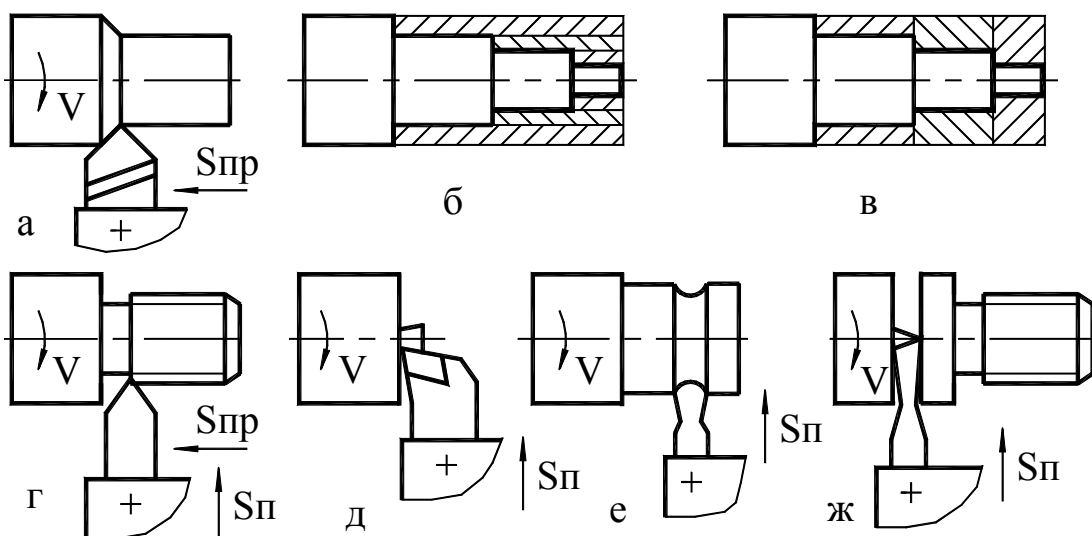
Обработка наружных поверхностей на токарных станках:
